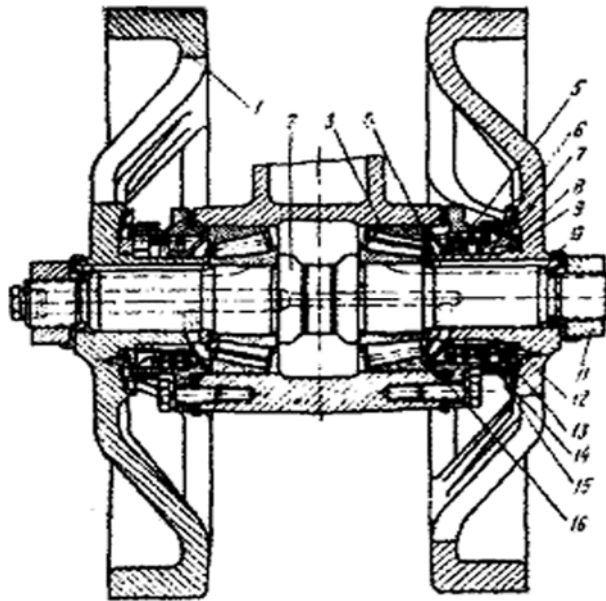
Опорний коток: 1- коток опорний; 2 - вісь; 3 - підшипник; 4- шпонка; 5 - корпус ущільнення; 6 - кільце ущільнювальне; 7 - кільце рухоме; 8 - кільце рухоме; 9,10 - кільця; 11 - гайка; 12 - штифт; 13 - стакан стопорний; 14 - пружина; 15 - лабіринт; 16 - кільце ущільнювальне.
